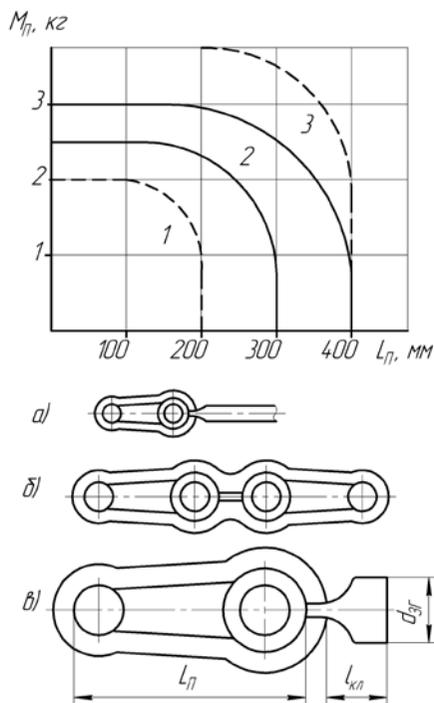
Диаграмма пределов применения различных заготовок: зоны штамповки: 1- штамповка от прутка, 2- с поворотом заготовки 3 — из отдельной заготовки
